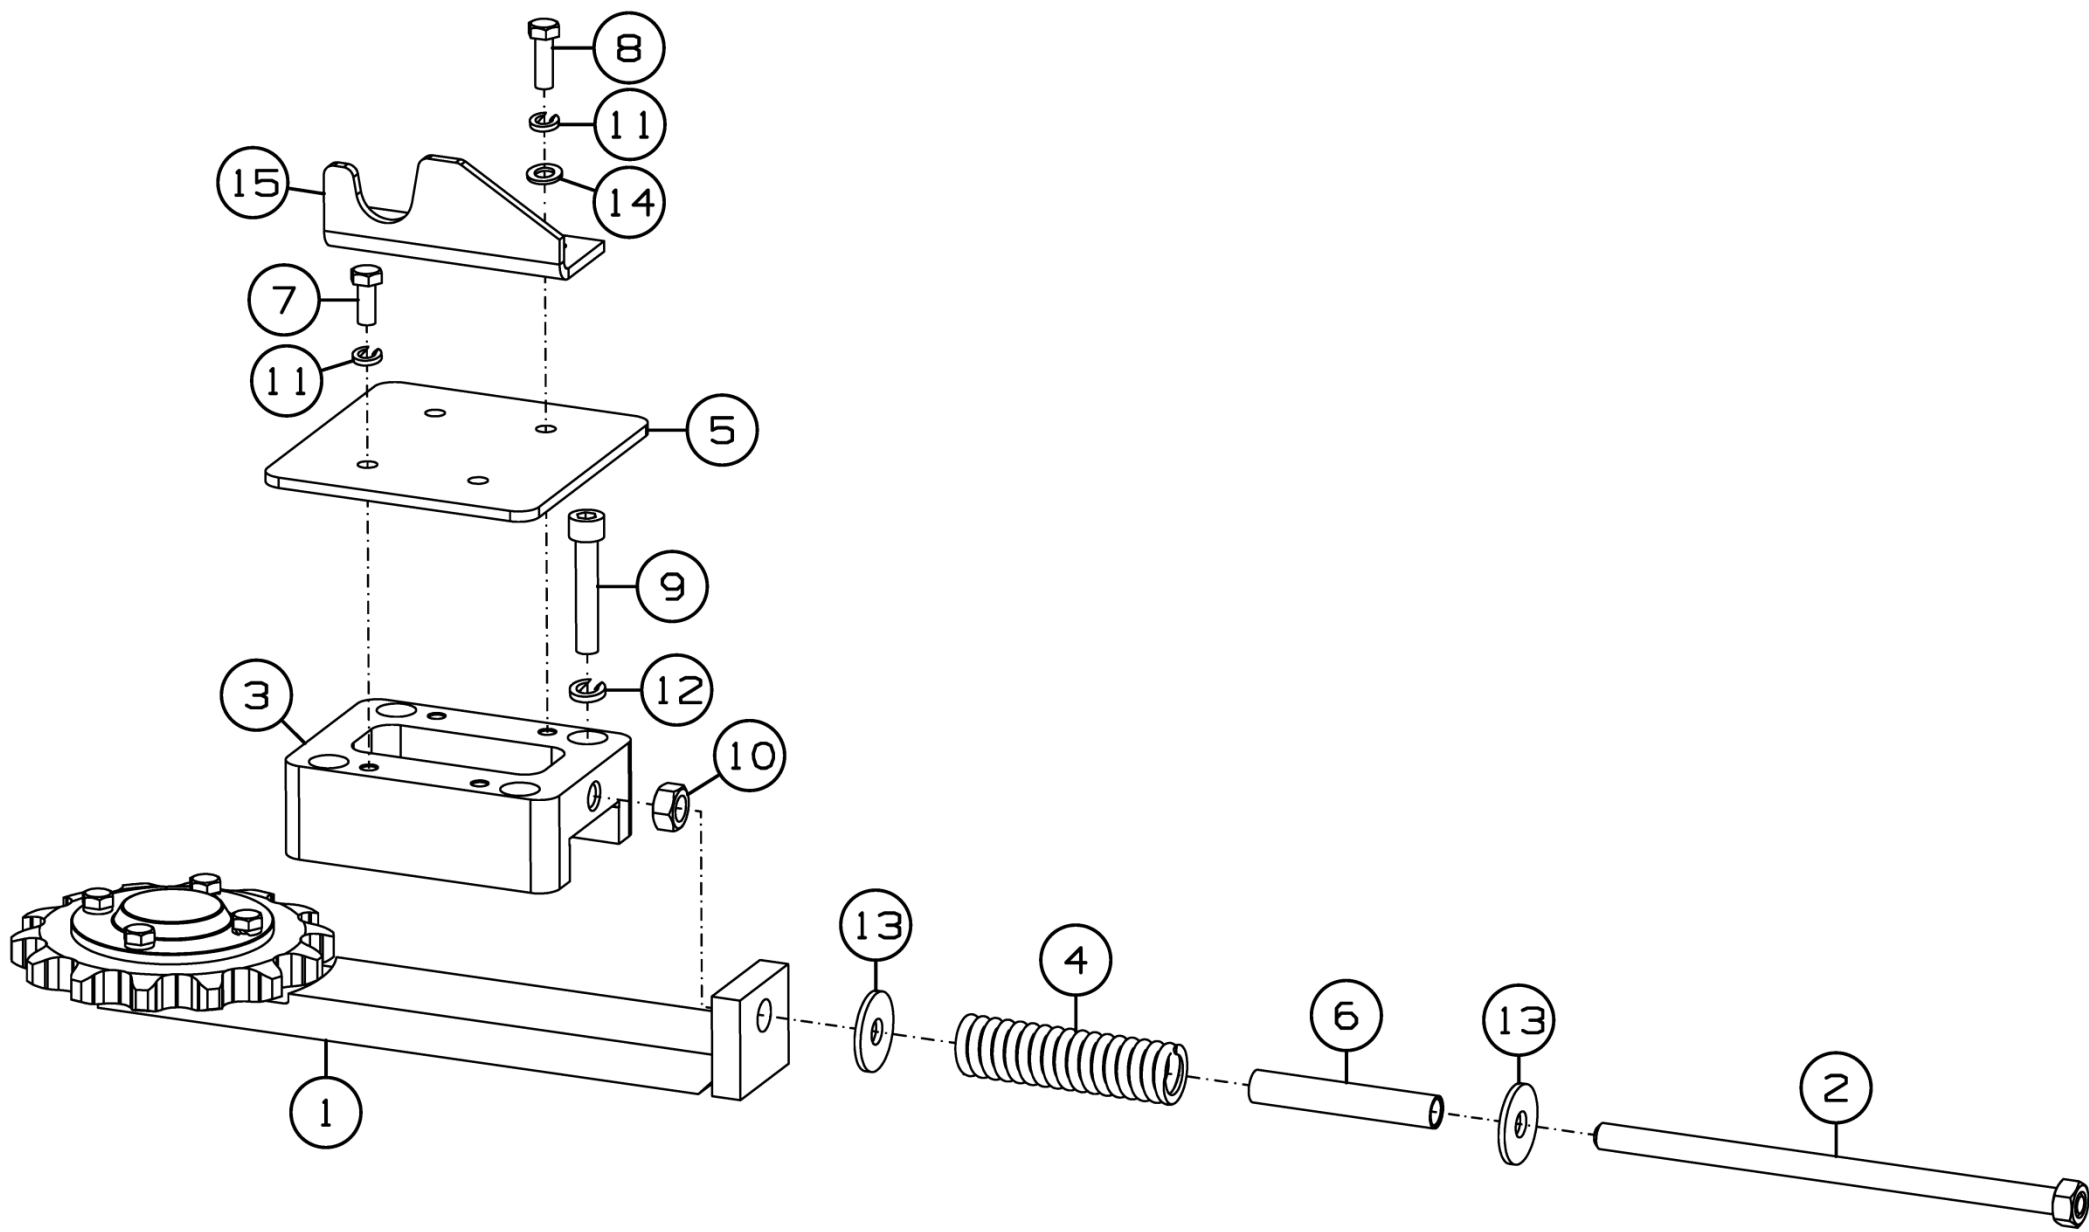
Установка натяжного устройства ППК-870.01.06.110А
